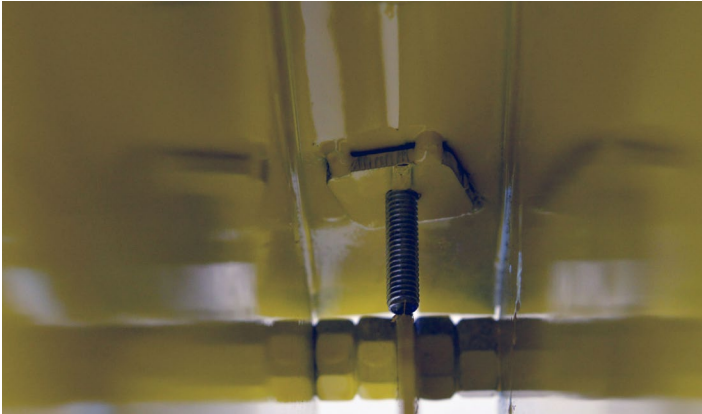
Detalhe do manipulador com o protetor de serra levantado
